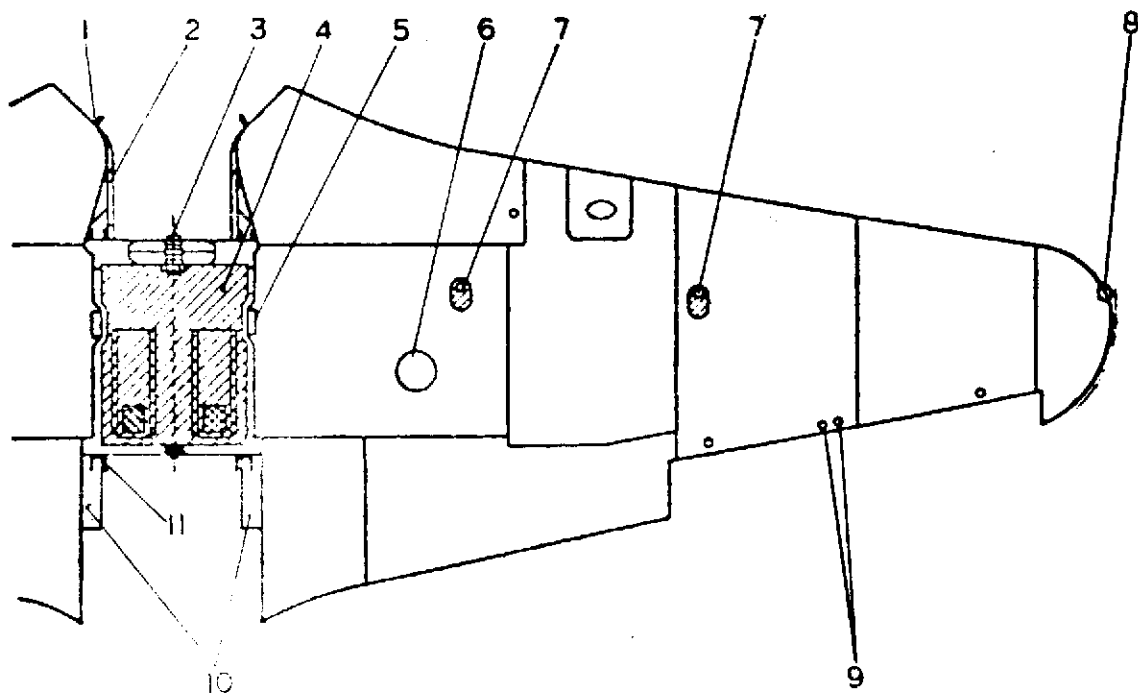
СХЕМА КРЫЛА (ВИД СВЕРХУ)
